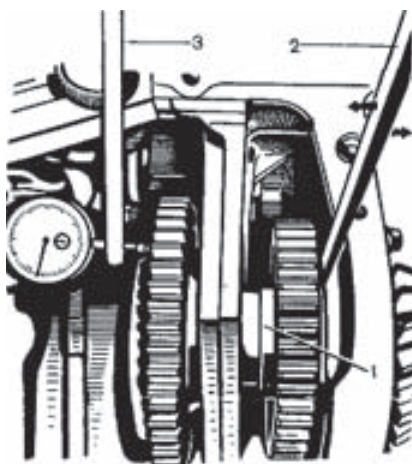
Проверка осевого зазора в подшипниках вторичного вала: 1 — вторичный вал; 2 — монтажная лопатка; 3 — индикатор.
